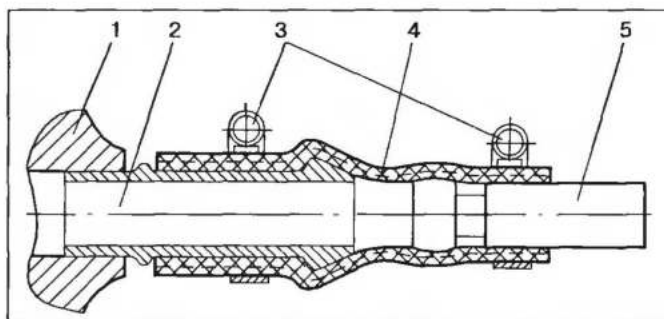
Простейший способ глушения штуцеров и патрубков рубашки охлаждения для опрессовки головки блока:
